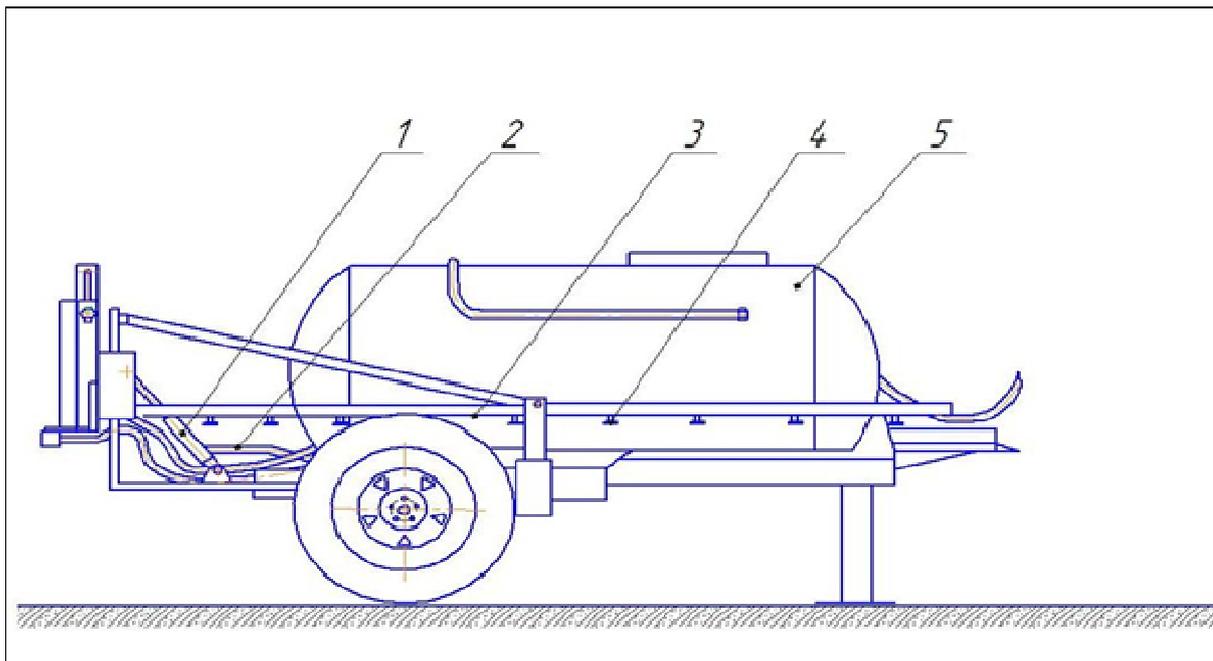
Штанговый малообъемный прицепной опрыскиватель «Заря-2000-ОП-02
